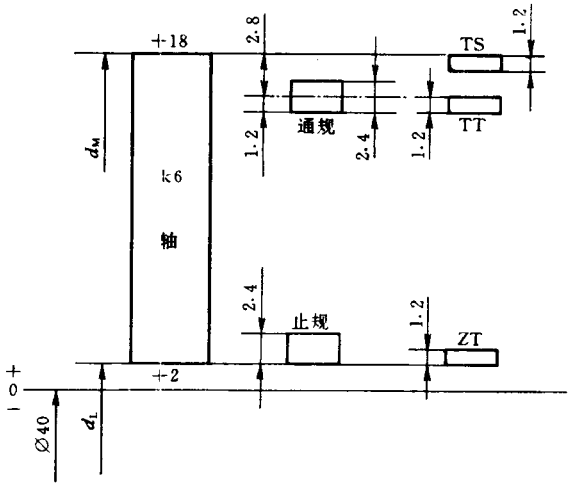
$\varnothing 40k6$  ⑤轴颈用工作量规及其校对量规定形尺寸公差带示意图
